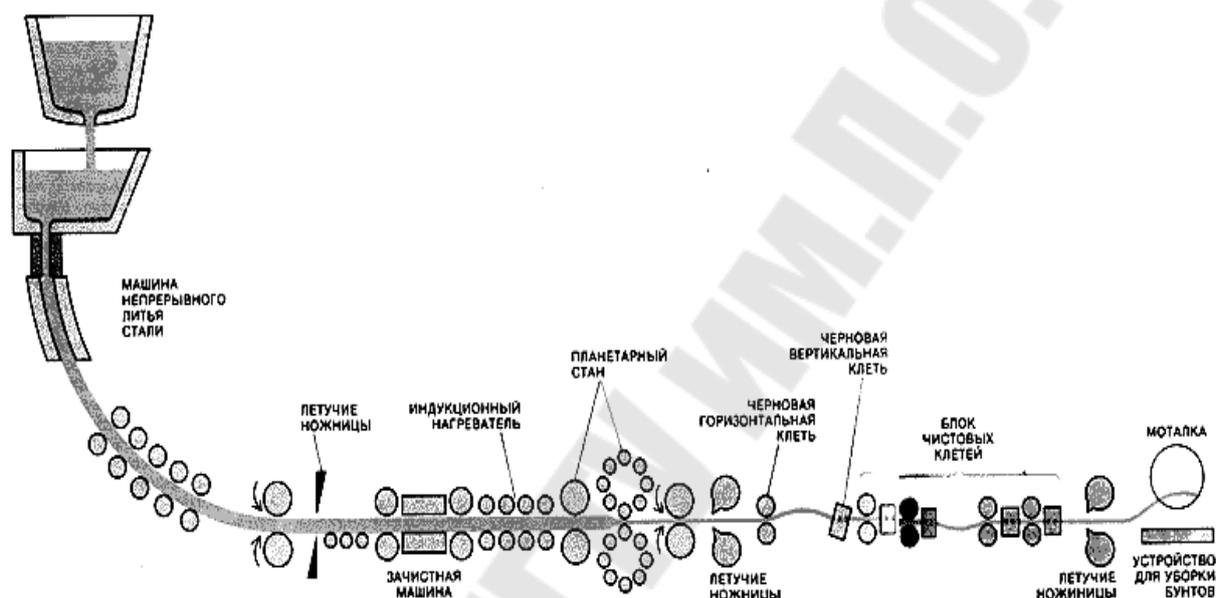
Схема литейно-прокатного агрегата для производства стальной проволоки:
